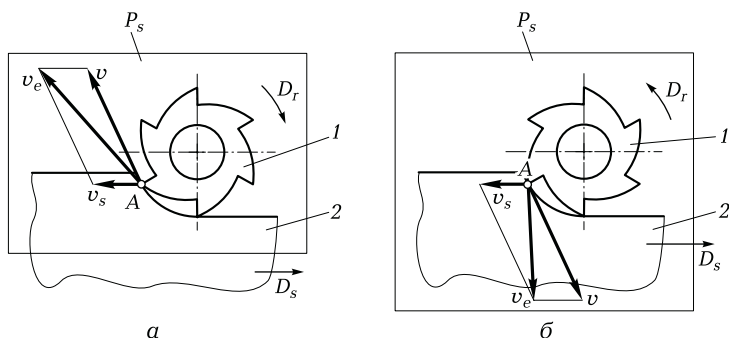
Элементы движений при встречном (а) и попутном (б) фрезеровании цилиндрической фрезой:
